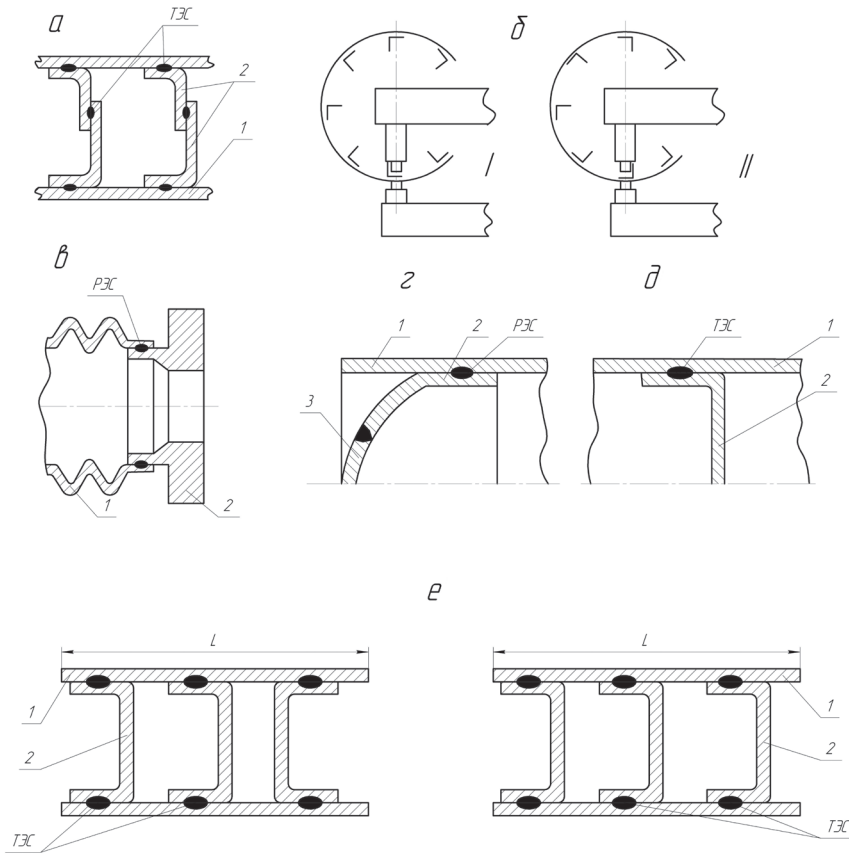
Примеры конструкций, выполняемых контактной сваркой
